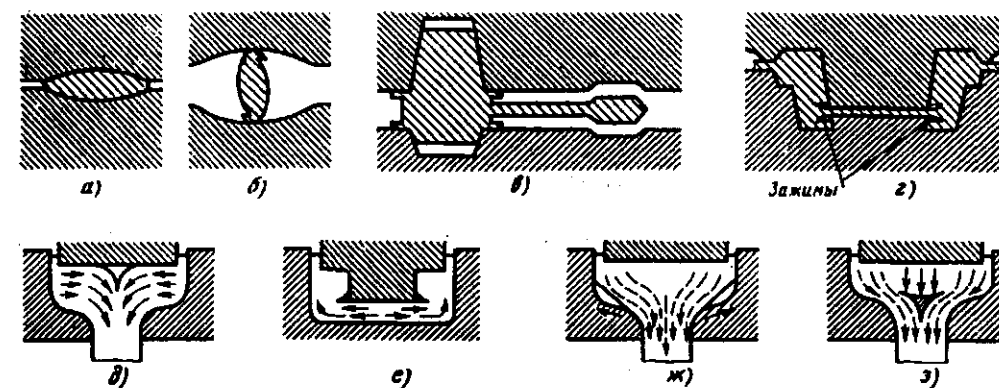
Дефекты штампованных заготовок: а, б – зажимы; в, д – зажим типа "прострел"; г – утяжка; е, ж – наружные и внутренние сколы
